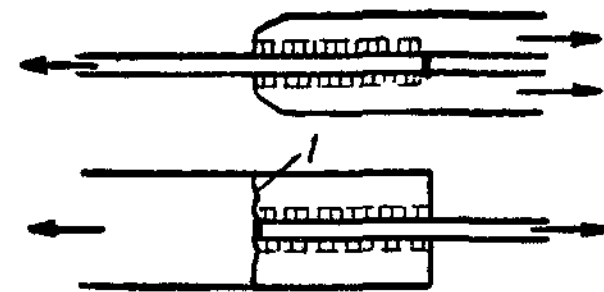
Разрушение основного металла у сближенных фланговых швов
